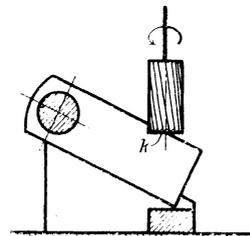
Einfräsen der Keilnuten für Gegengewichte.
